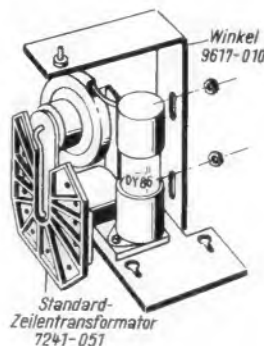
Der Montagewinkel wird durch zwei zusätzliche Schrauben am Standard-Zeilentransformator befestigt
